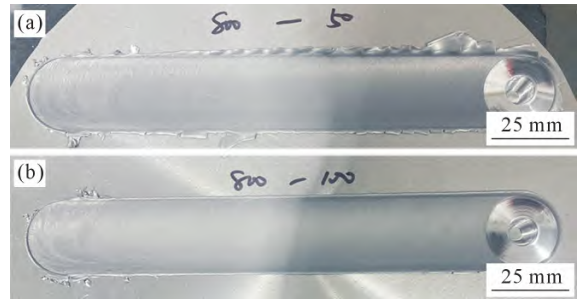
焊缝表面宏观形貌:(a) FSP50; (b) FSP100
